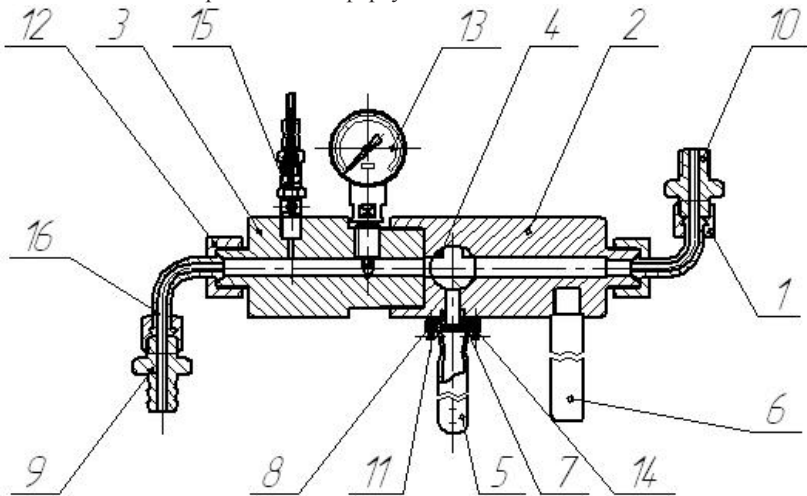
Прибор для проверки ТНВД: 1 – гайка специальная; 2 – корпус; 3 – корпус приборов; 4 – кран трехходовой; 5 – пробирка мерная; 6 – ручка; 7 – фланец верхний; 8 – фланец нижний; 9 – штуцер входной; 10 – штуцер выходной; 11 – болт; 12 – гайка; 13 – манометр; 14 – прокладка; 15 – моментоскоп; 16 – трубка.
